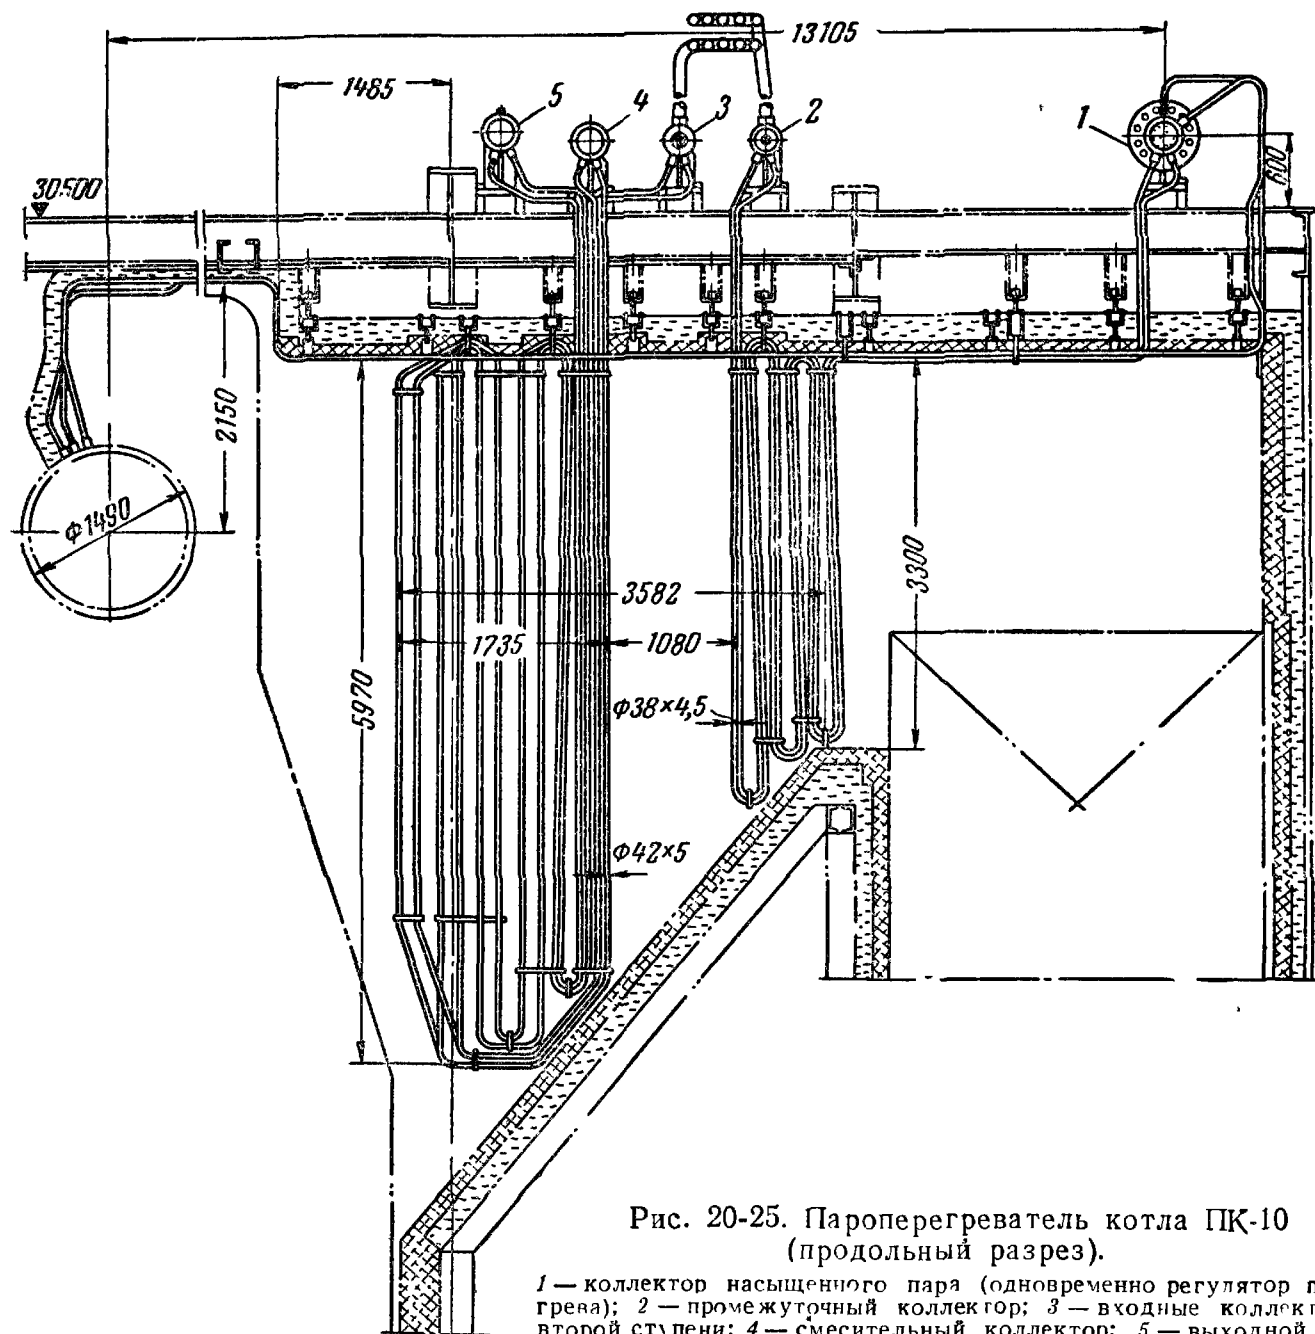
Пароперегреватель котла ПК-10 (продольный разрез).
